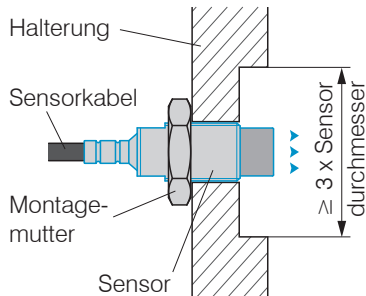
Flächenbündige Montage eines ungeschirmten Sensors in einer metallischen Halterung mit Aussparung
